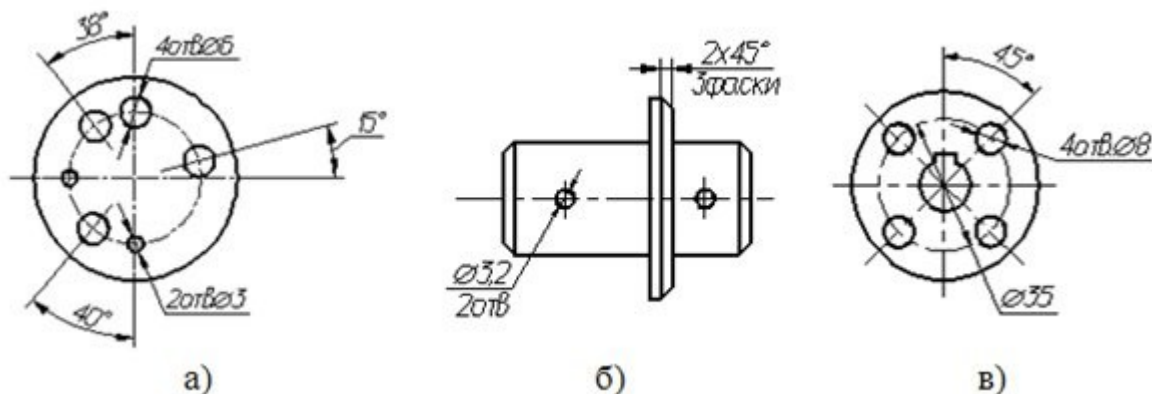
Примеры нанесения размеров одинаковых отверстий
